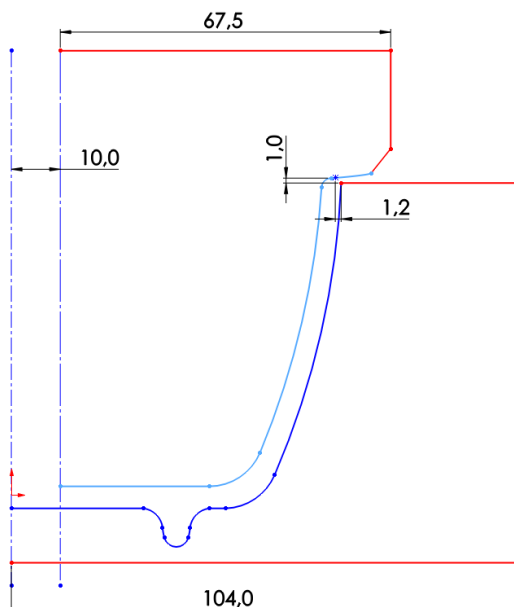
Desenho do molde, a azul-escuro, e do calibrador, a azul-claro, necessários na conformação por Roller da tigela do projeto (dimensões em mm).
